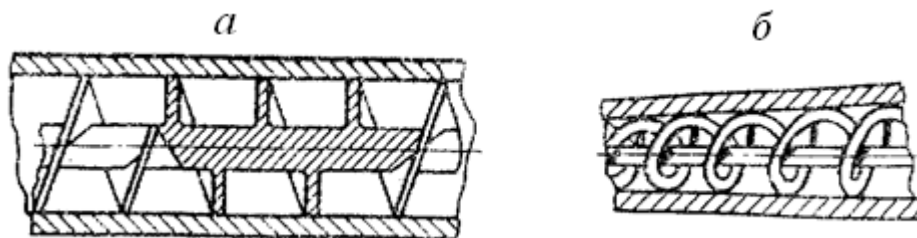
Конструкции цилиндрической части корпуса винтового экструдера с лопастным (а) и ленточным (б) винтами
